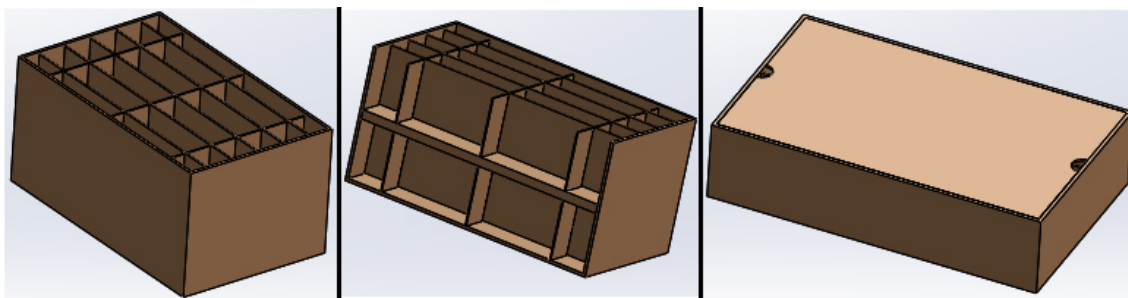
Modelação 3D da nova proposta para a embalagem do cliente D – Embalagem completa, corte de plano frontal e corte de plano vertical (separação de níveis)
